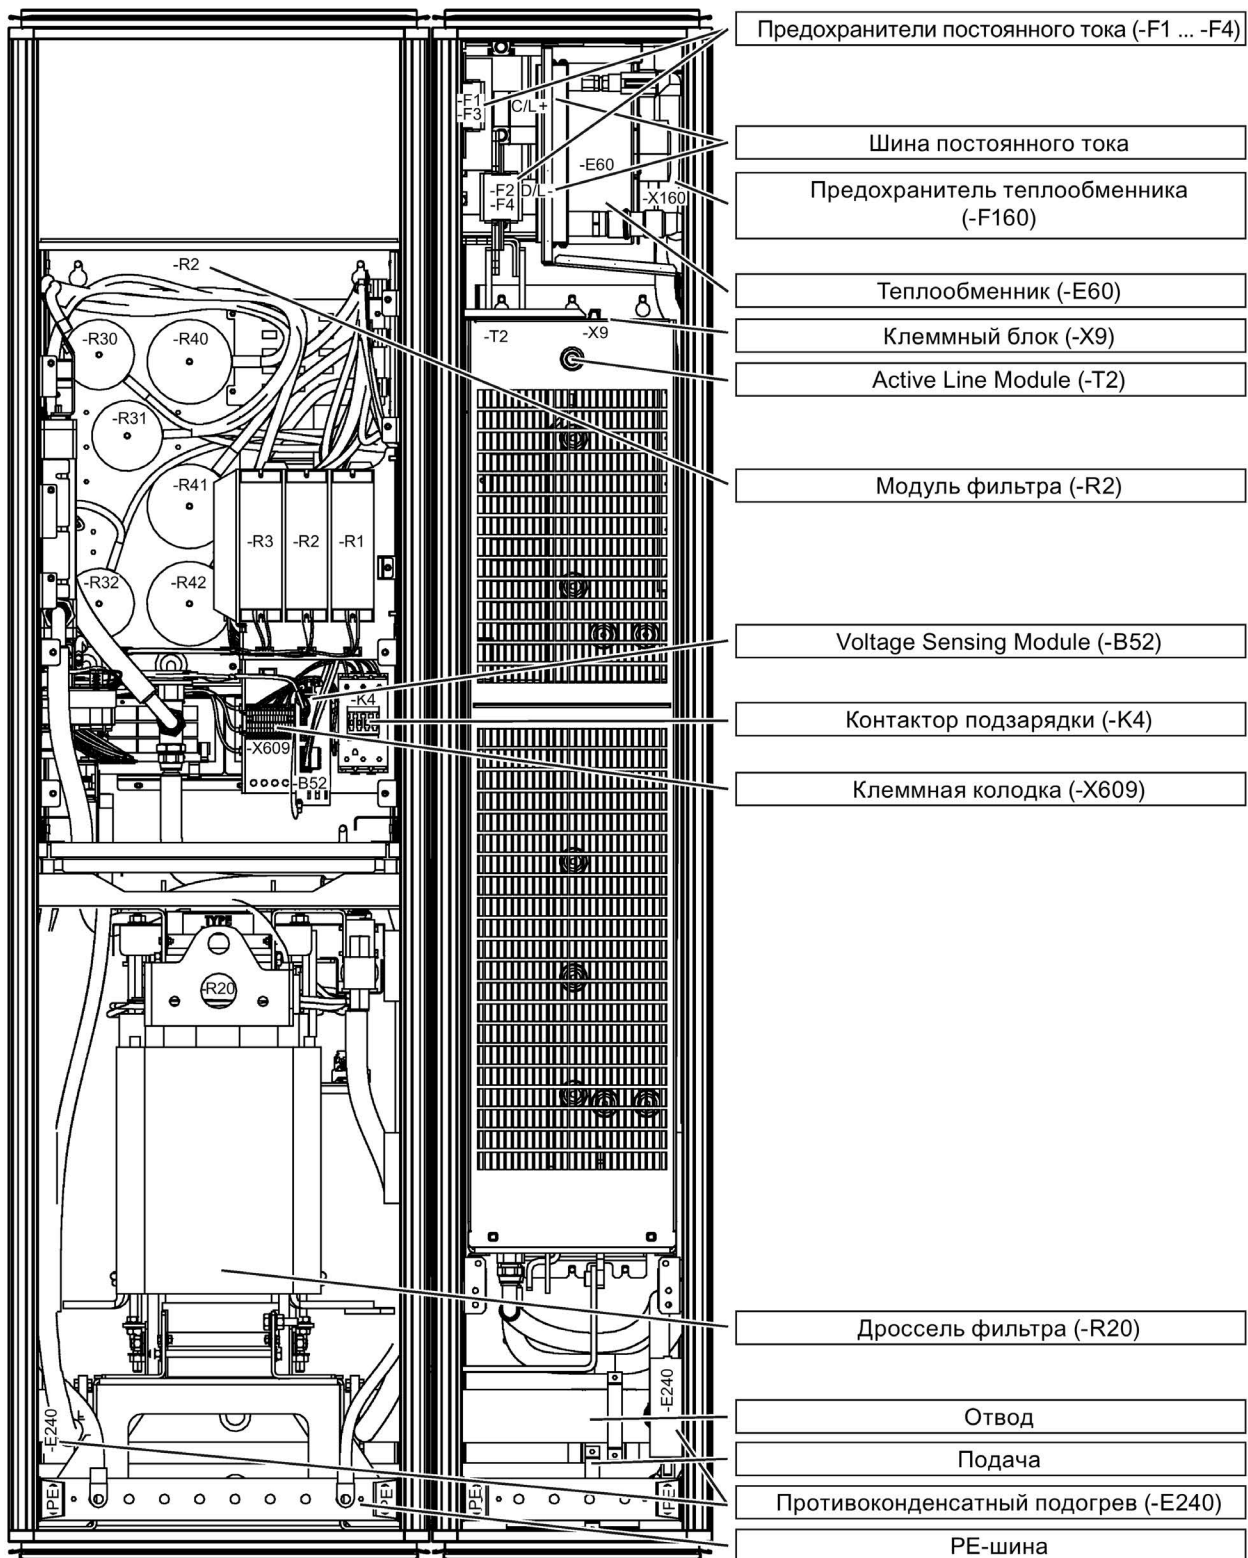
Примеры сборки активного интерфейсного модуля (типоразмер J1L) и активного модуля питания (типоразмер JXL)
